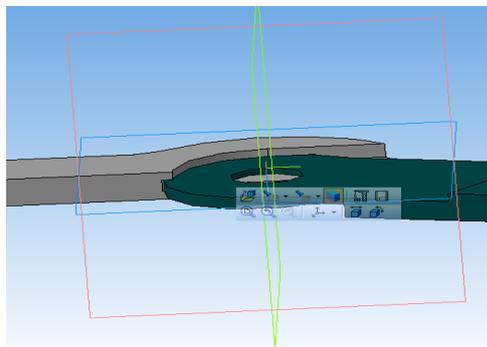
3D модель узла ортеза (в разрезе, вид сверху)
